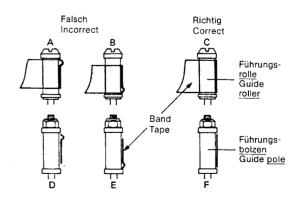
Führungsrolle und Führungsbolzen Fig. 4-4 Guide roller and guide pole
